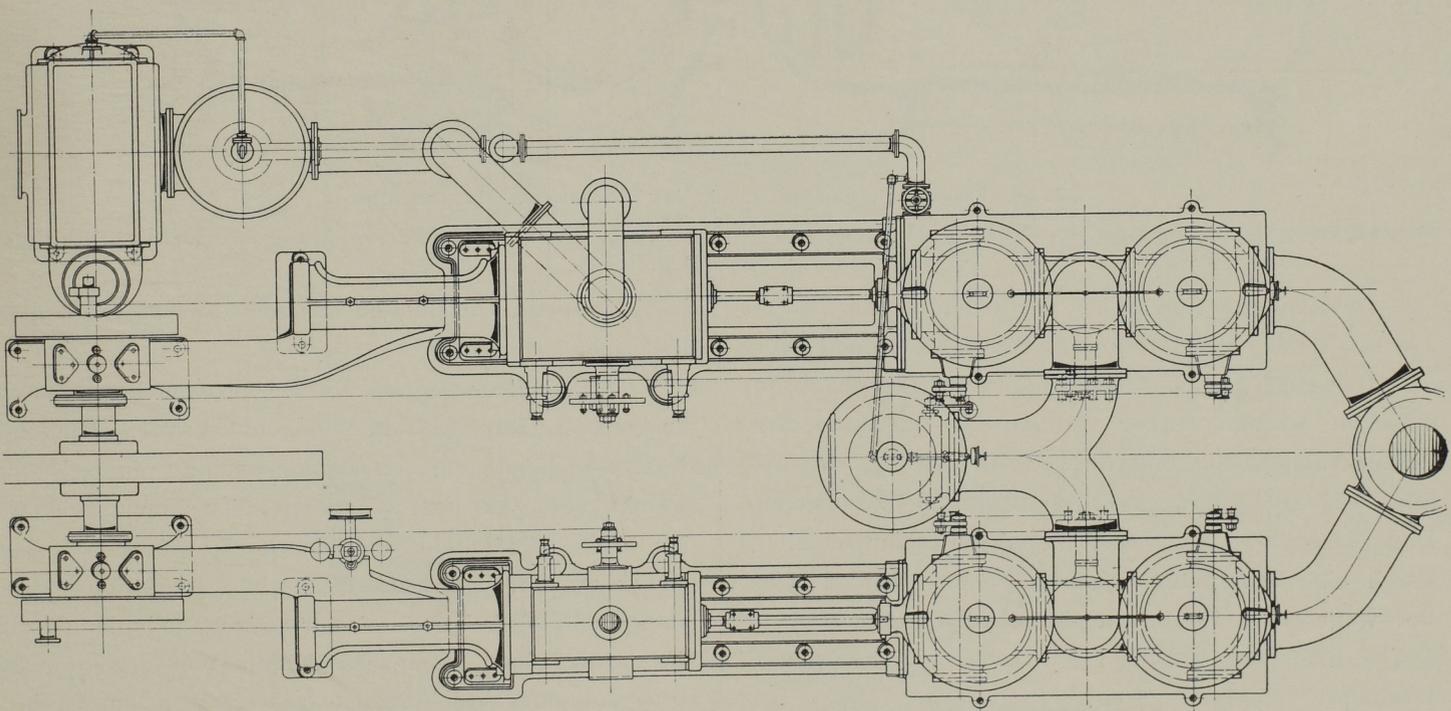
Grundriss der Pumpmaschine. Masst. 1:64.
